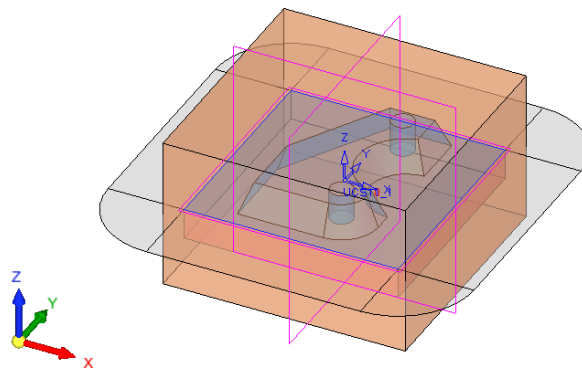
Заготовка для будущих матрицы и пуансона
